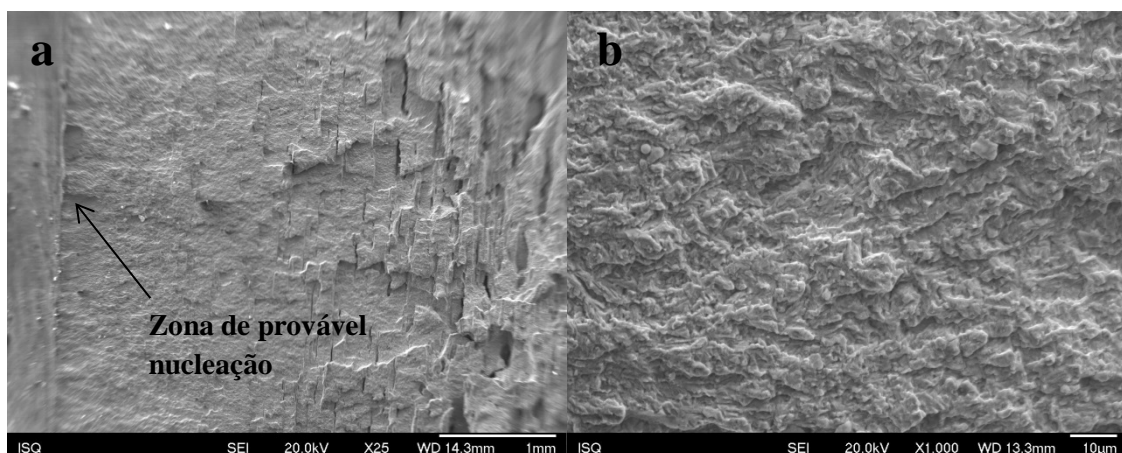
Ilustração sobre superfície de fratura do provete aço S355 J2; a) Superfície geral do provete, b) Zona de iniciação de fadiga.
